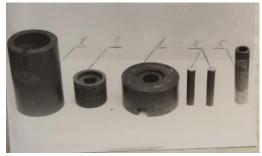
Приспособление для сварки кольцевых образцов: 1 - основание; 2 - корпус; 3 - втулка; 4 - образцы; 5 - шток;
